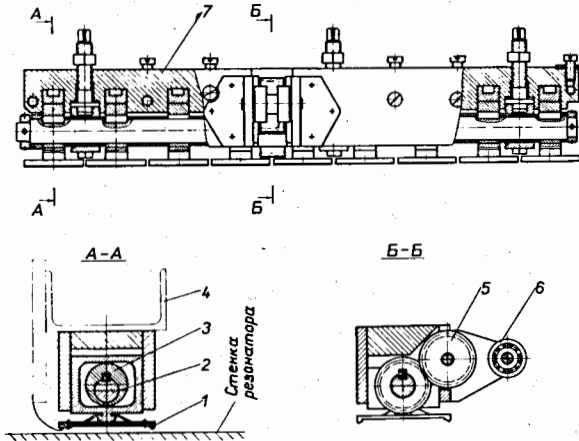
Закорачивающее устройство. 1 - контактная пластина, 2 - вал, 3 - эксцентрик, 4 - каркас подвижной панели, 5 - шестерня, 6 - опорный подшипник, 7 - корпус.
